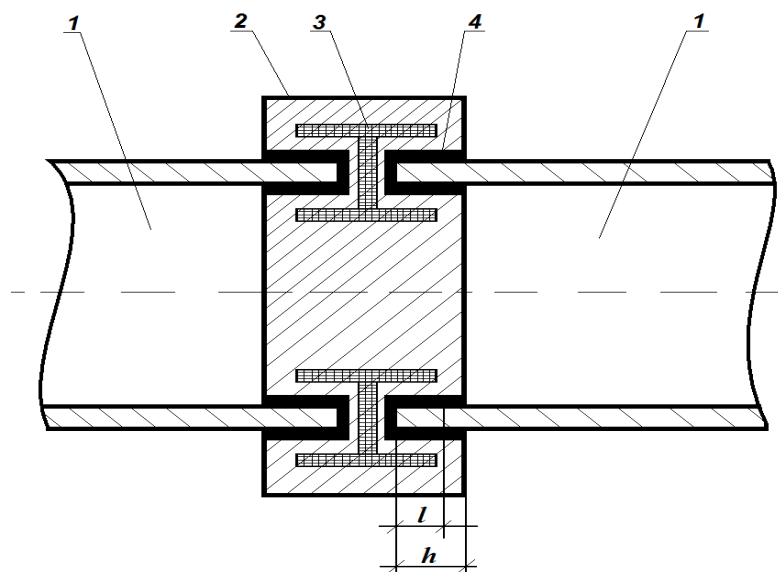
Схема предварительного нагрева торцов свариваемой полимерной трубы
